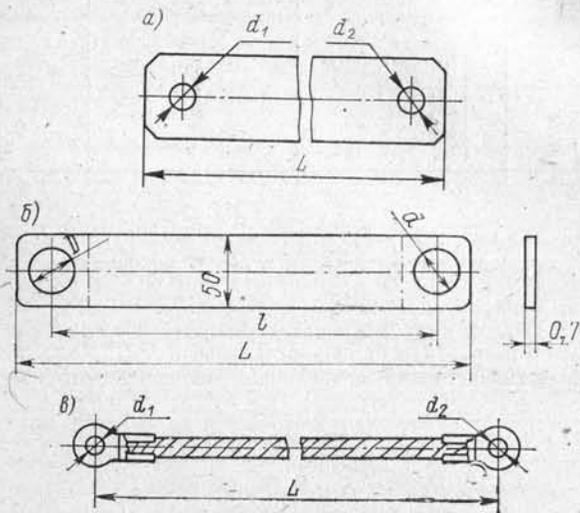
Перемычки для заземления корпусов электрооборудования: а — типа ПпМ; б — типа ПпЛАКС; в — типа ПгМ.
